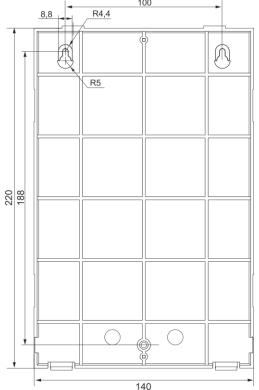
Установочный чертеж основания корпуса P485, RS485/FTTx-S-SC
